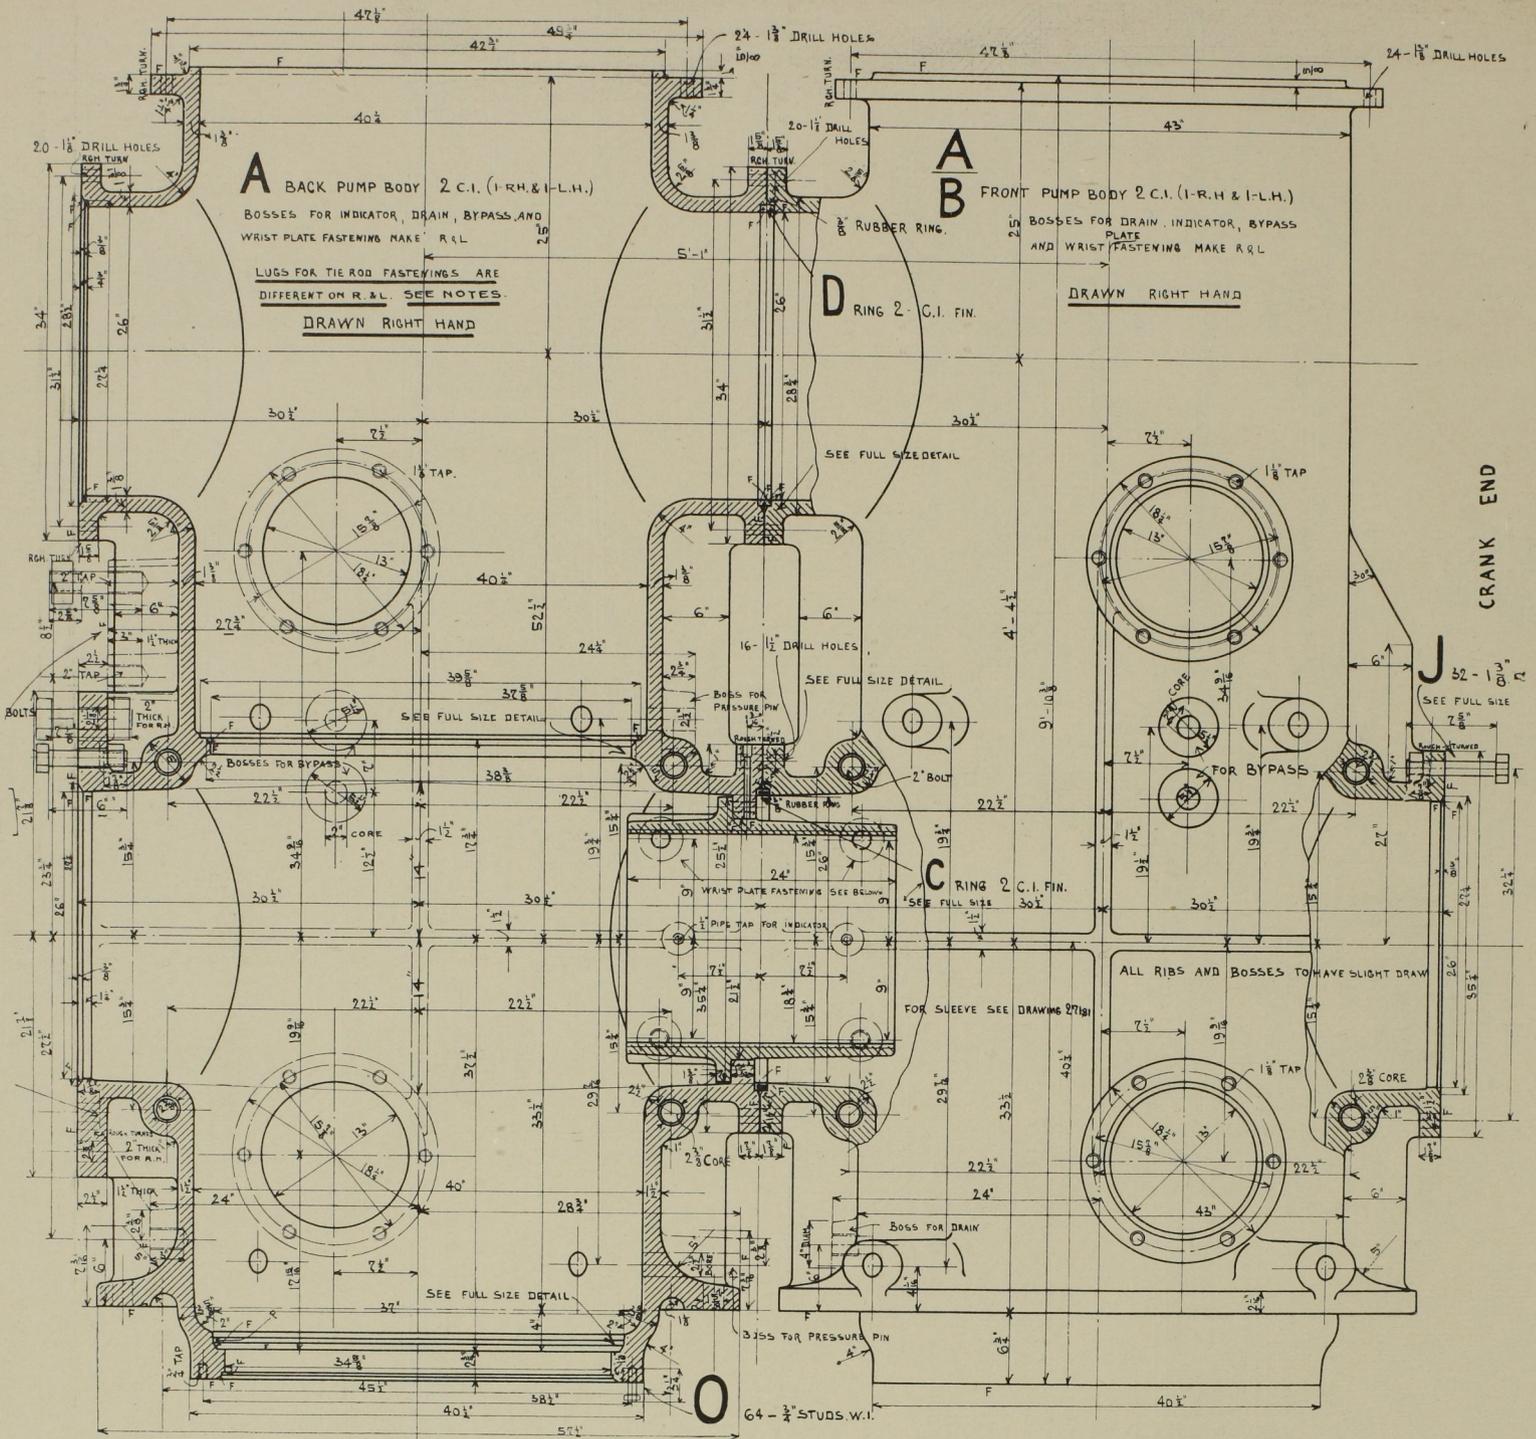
Werkzeugzeichnung der Hochdruckpumpe. Längsschnitt. Masst. 1:16.
